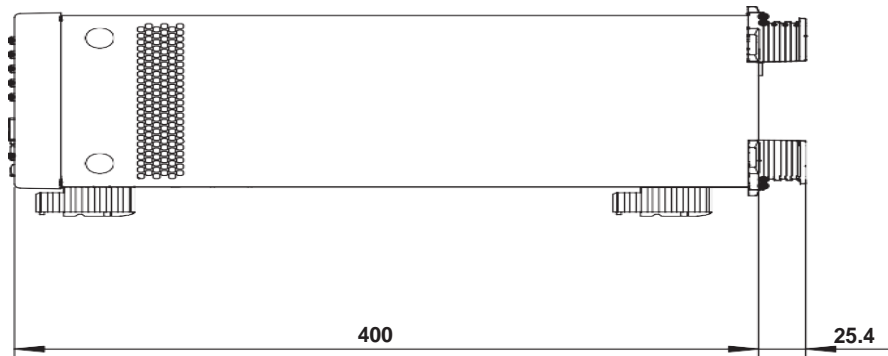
Dimensiones de la parte lateral del sistema del controlador de cuadros YOKOGAWA serie AQ2211. Fuente: [17].
